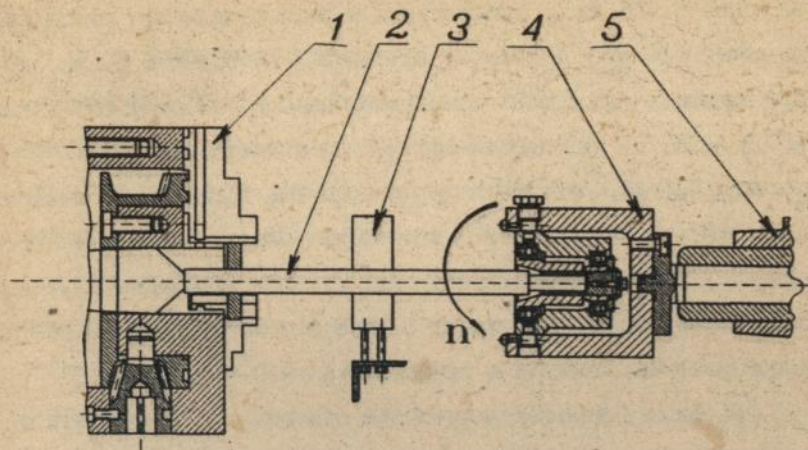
Схема закрепления нежесткой заготовки и исполнительного органа в токарно - винторезном станке 1М62П: 1 - шпиндель; 2 - нежесткая заготовка; 3 - НИВ; 4 - исполнительный орган; 5 - задняя бабка.
